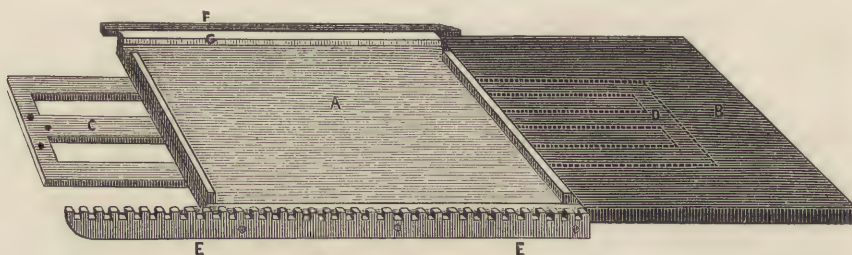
Marbre, table à encrer, crémaillère, supports, chemins.
